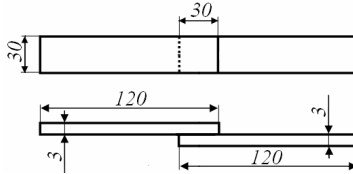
Схема сборки деталей для пайки и точечной сварки
